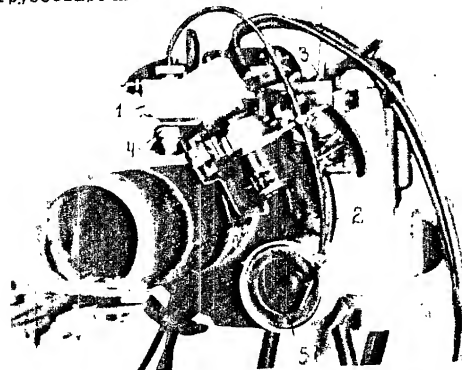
Трубосварочный автомат для неповоротных стыков МВТУ-4.
